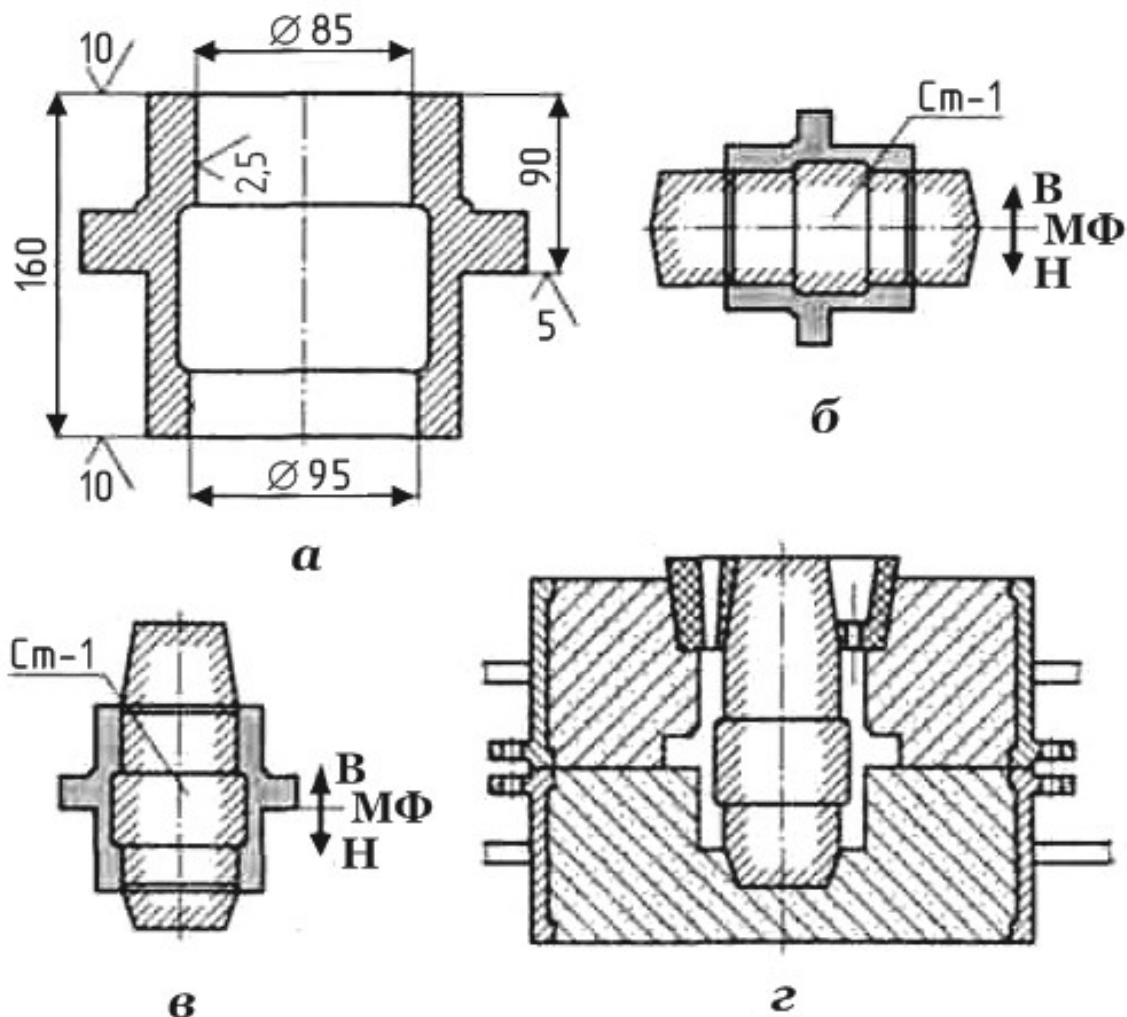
Разработка технологического процесса изготовления отливки корпуса подшипника: а – чертеж детали; б, в – варианты технологии; з – собранная форма; Ст-1 – стержень; МФ – разъем модели и формы; В, Н – верх и низ
